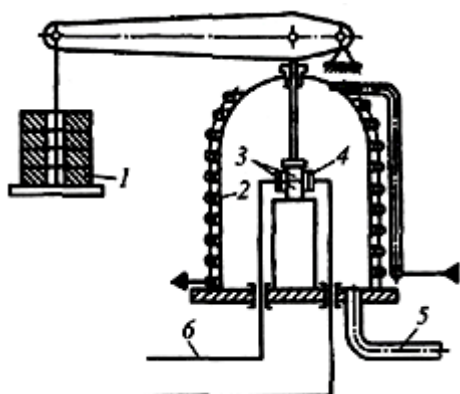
Схема диффузионной сварки: 1- механическое устройство для сжимающего давления, 2- металлическая камера, 3 – свариваемые заготовки, 4-индуктор, 5- ввод к вакуумному насосу, 6- ввод к высокочастотному генератору.
